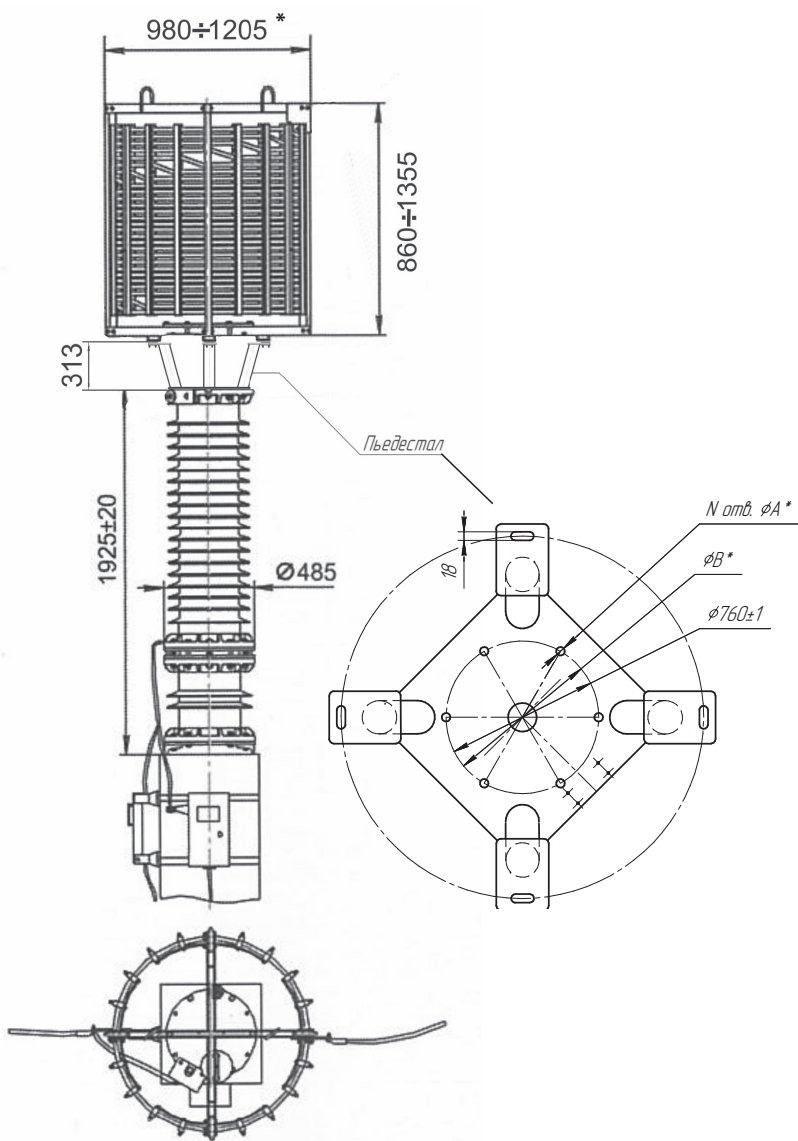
Установка заградителей ВЗ-630, ВЗ-1250, ВЗ-2000 на конденсатор связи усиленного исполнения СМА - 110/√3 - 6,4 УХЛ1.
